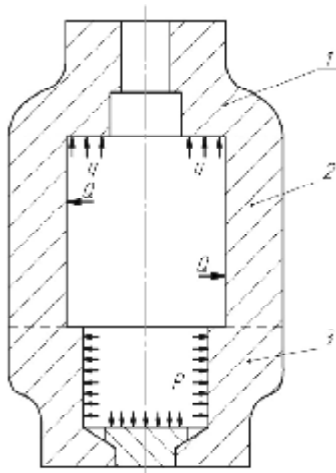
Розрахункова схема станини: 1 – верхня частина (поперечка); 2 – стійка; 3 – нижня частина (циліндр)
